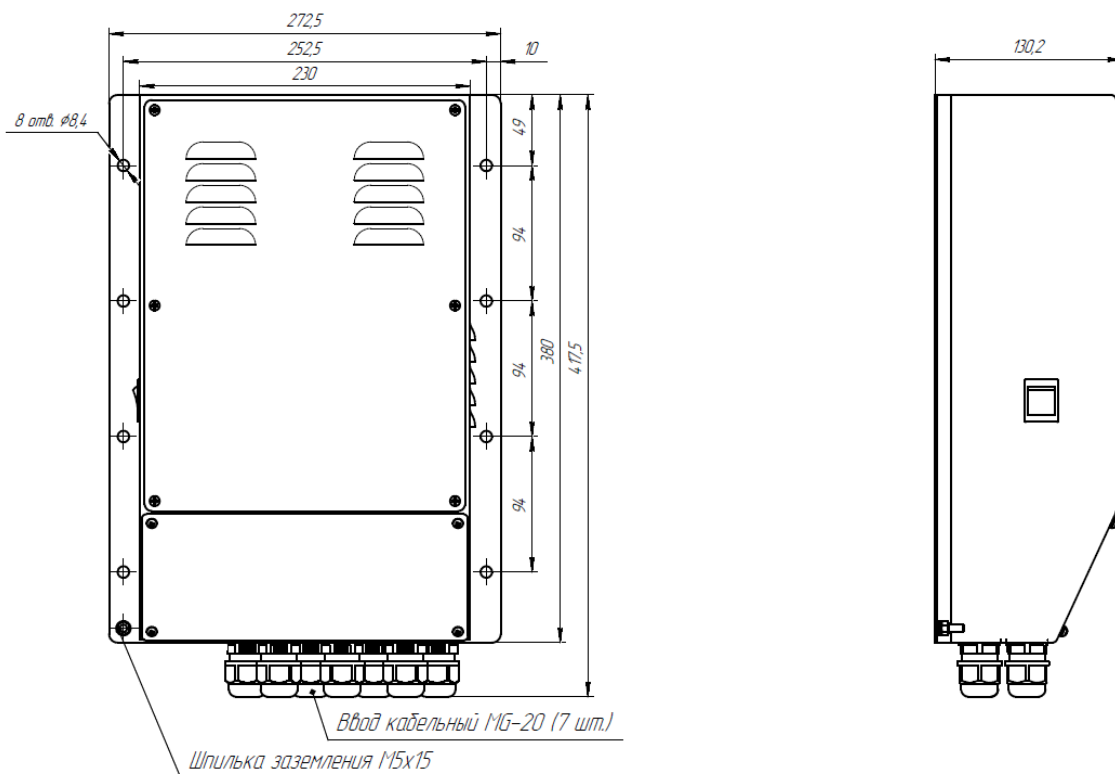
Габаритные и установочные размеры БП-103-20
